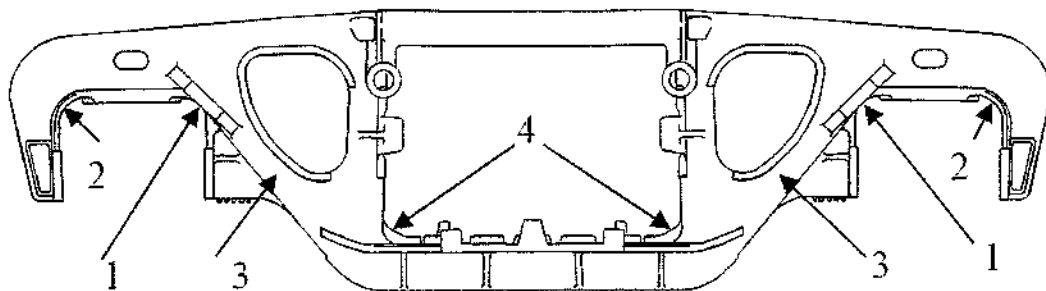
Загальний вигляд рами бокової, кресленик 100.00.002-4
